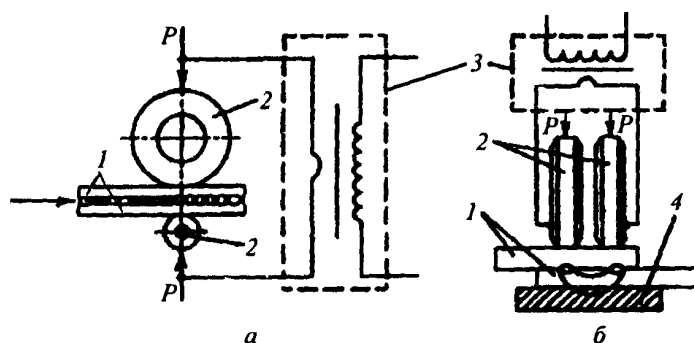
Схема шовной двусторонней (а) и односторонней (б) сварки: 1 — свариваемые детали, 2 — сварочные ролики, 3 — сварочный трансформатор, 4 — медная прокладка
